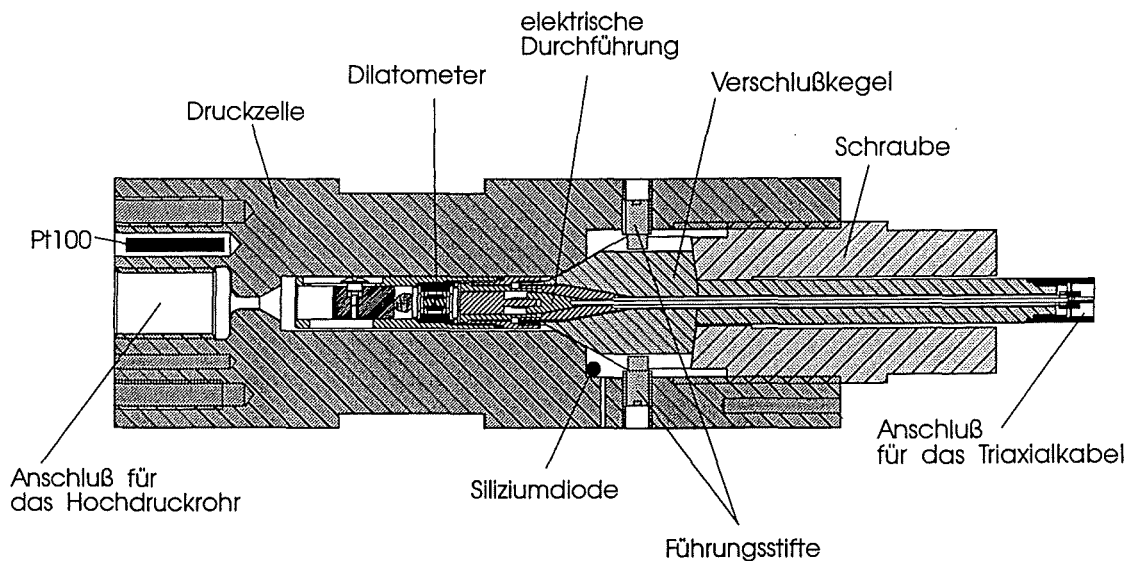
Schnitt durch die Druckzelle mit dem eingebauten Dilatometer. Die Druckzelle hat einen Durchmesser von 30 mm und eine Lnge von 100 mm.
